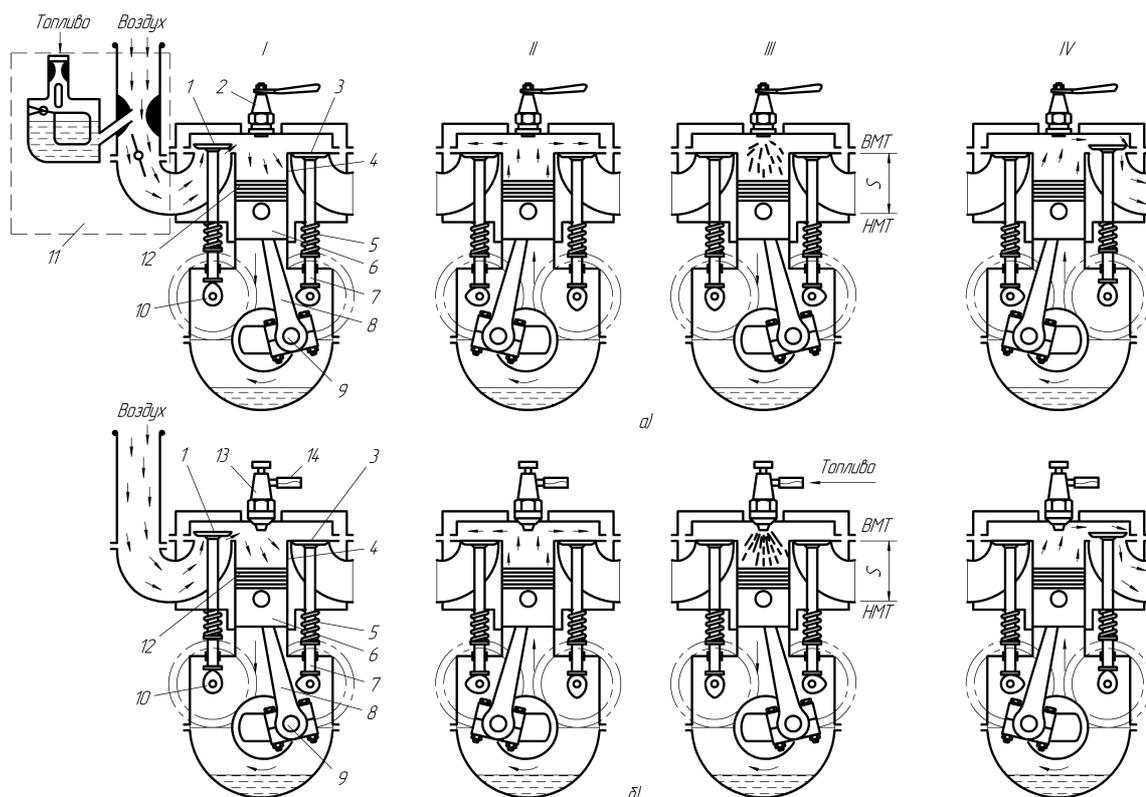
Схема четырехтактных двигателей внутреннего сгорания: а – карбюраторного; б – дизельного; I – всасывание; II – сжатие; III – рабочий ход; IV – выхлоп; 1 – впускной клапан; 2 – свеча зажигания; 3 – выпускной клапан; 4 – цилиндр; 5 – пружина; 6 – поршень; 7 – толкатель; 8 – шатун; 9 – коленчатый вал; 10 – кулачковый распределительный вал; 11 – карбюратор; 12 – поршневые кольца; 13 – форсунка; 14 – топливопровод
